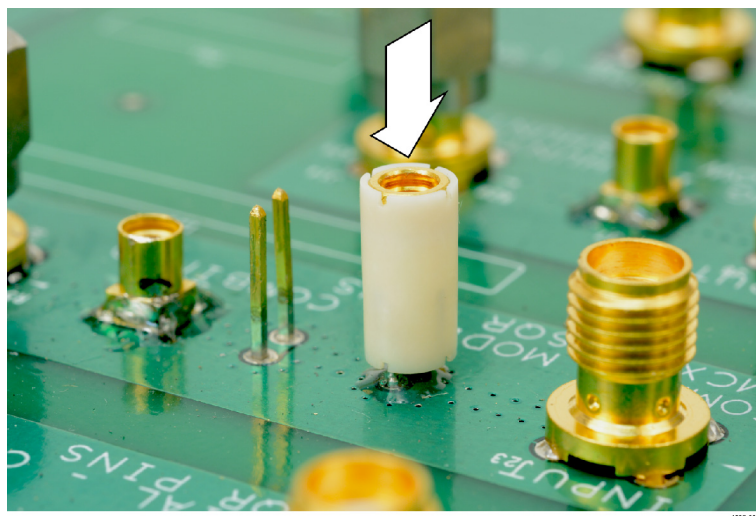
Установка адаптера MMCX — штыревые контакты с шагом 0,062" (1,57 мм) в рабочее положение.
